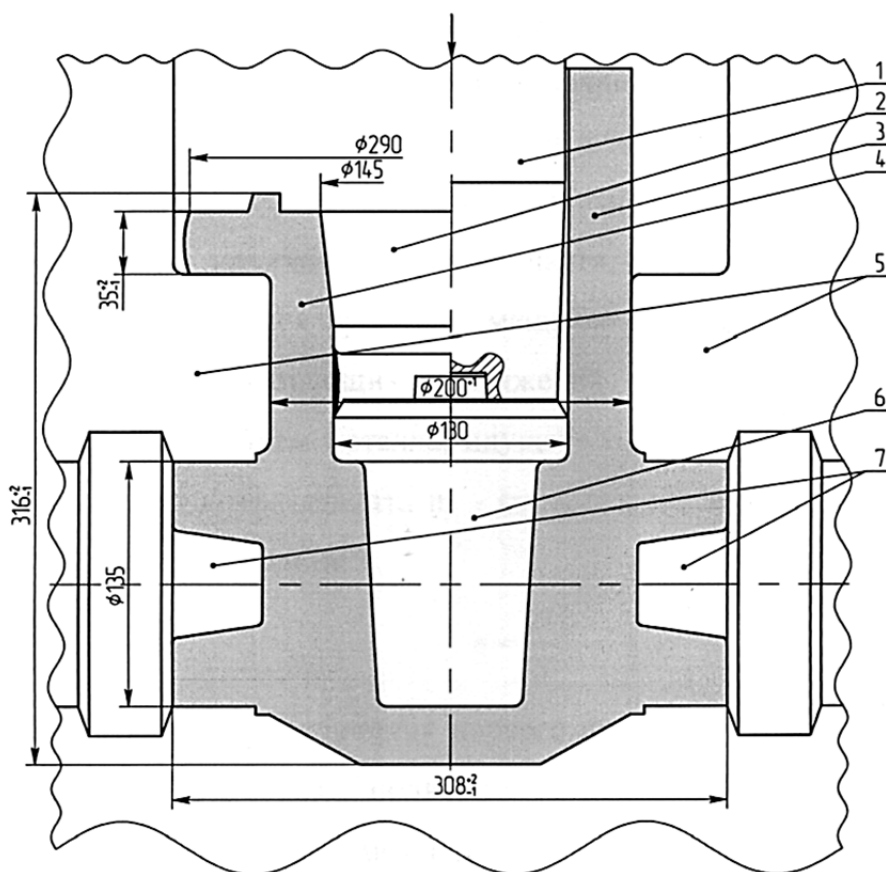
Схема штамповки корпуса ТД13075-100К1 из стали 12Х18Н10Т:
